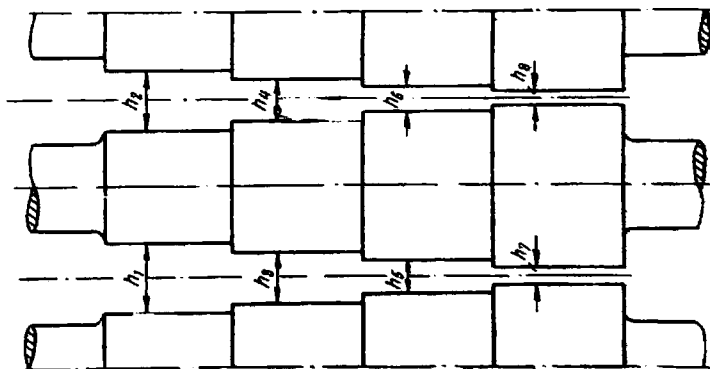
Ступенчатые валки для прокатки полосовой стали
